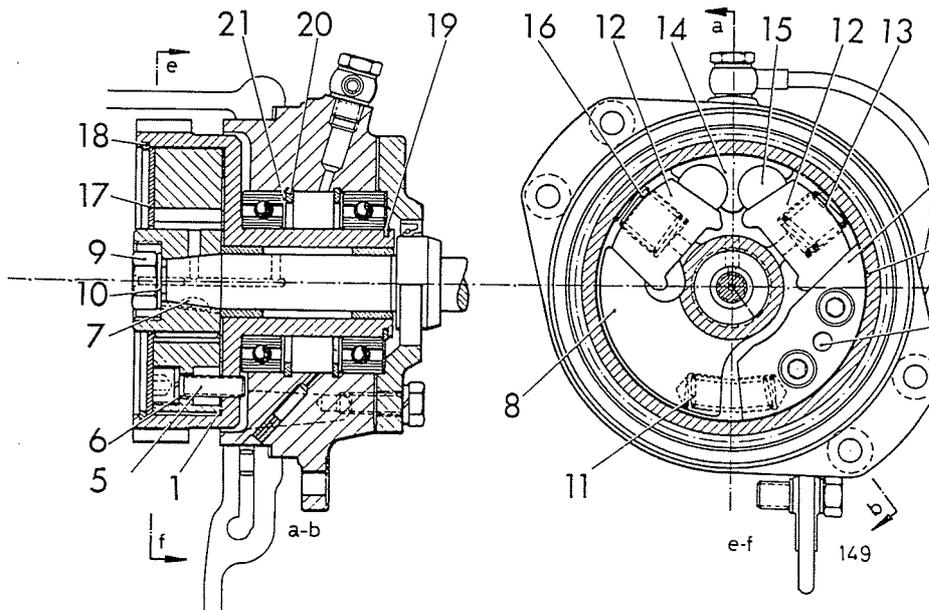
Spritzversteller F 4-6L 514 mit zwei Fliehgewichten und zwei Kugellagern
